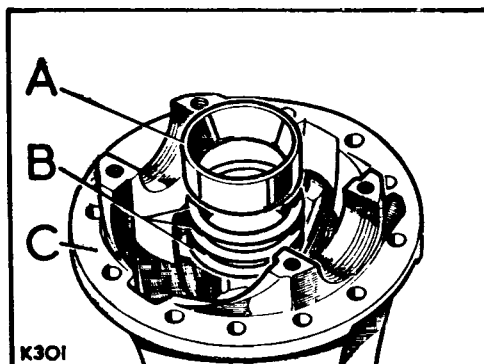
Pista exterior de cojinete de extremo del piñón.
